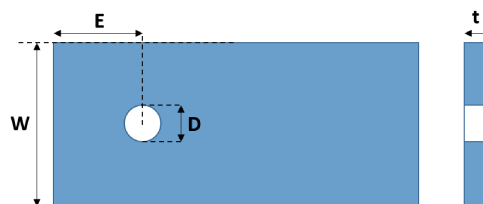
Paramètres géométriques des pièces assemblées dans les assemblages simple ou double recouvrement.
